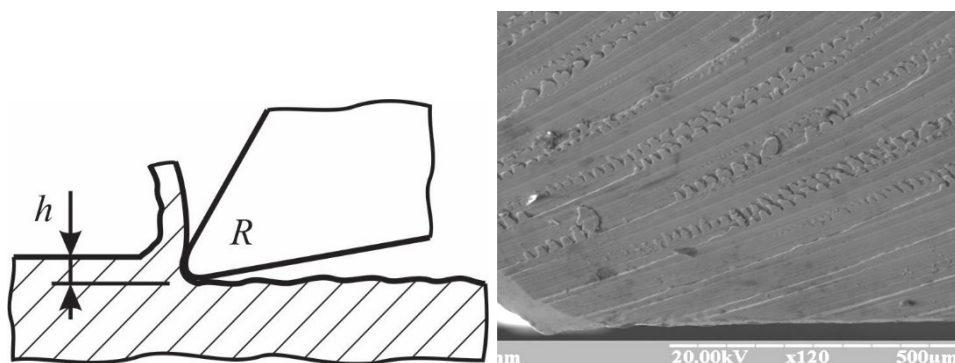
Поверхня, оброблена різцем з притупленою крайкою [274]
